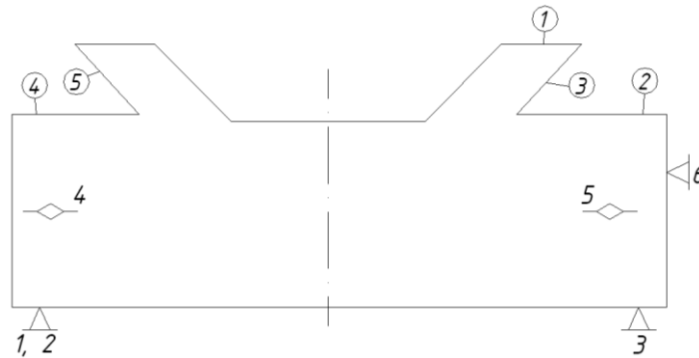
Теоретична схема базування при обробці чорнових баз
